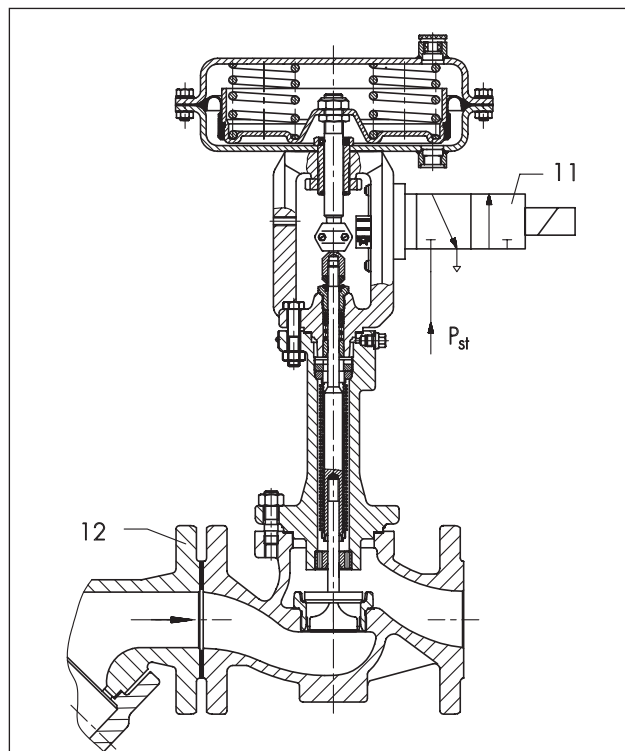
· Пневматический регулирующий и быстро закрывающийся клапан тип 241-1-газ
